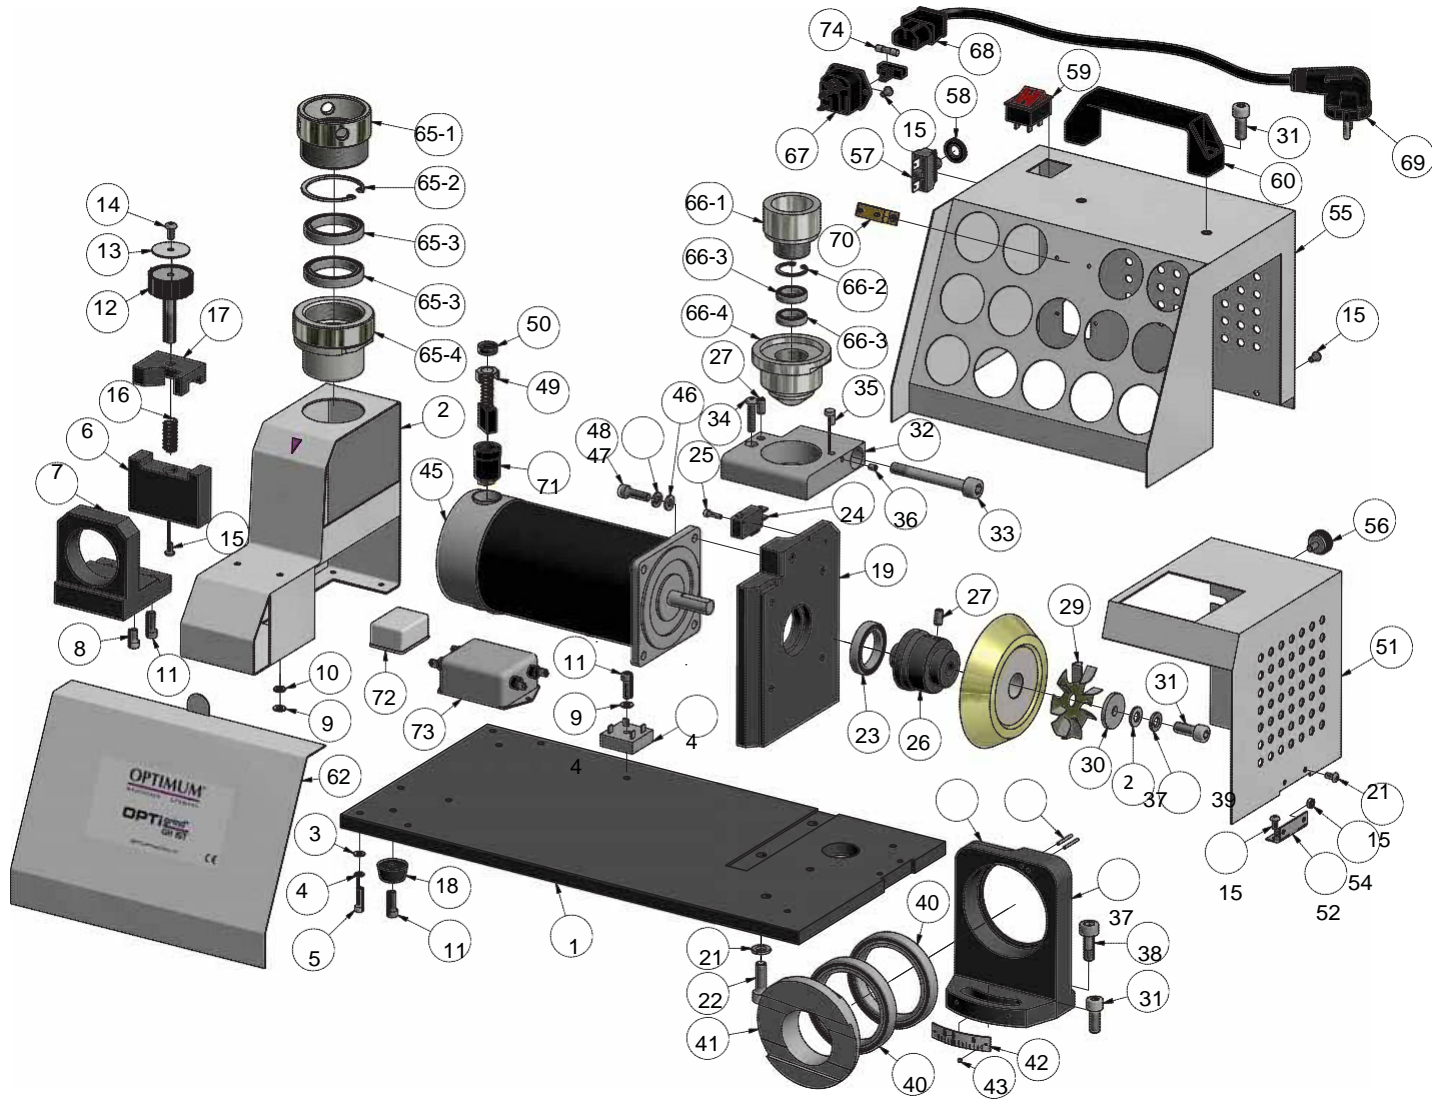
Ersatzteilzeichnung - Drawing spare parts 33
